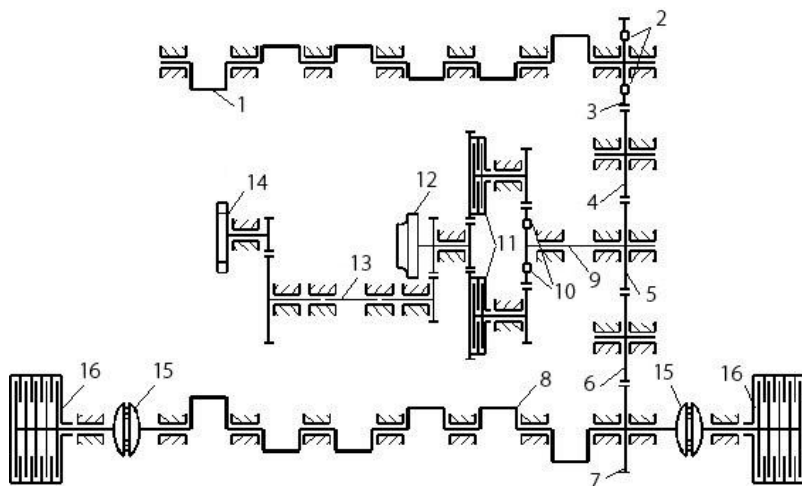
Кинематическая схема двигателей 6ТД-1, 6ТД-2 с потребителями. Цифрами на схеме обозначены: 1 – впускной коленчатый вал; 2 – упругая муфта на впускном валу; 3÷7 – шестерни главной передачи; 8 – выпускной вал; 9 – рессора привода компрессора; 10 – упругая муфта в приводе компрессора; 11 – фрикционные муфты; 12 – ротор компрессора; 13 – рессора привода турбины; 14 – ротор турбины; 15 – резино-пальцевые муфты; 16 – потребители (гидротормоза).
